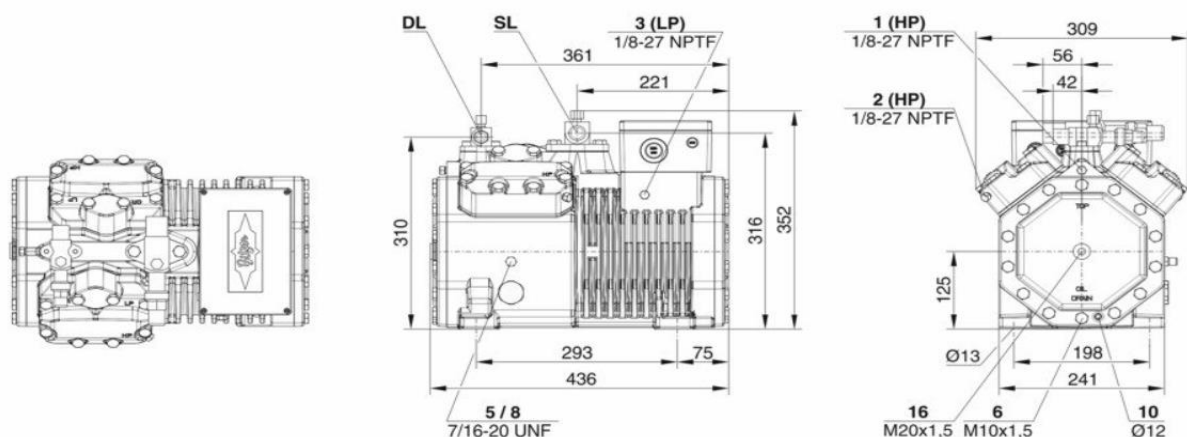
Габаритні розміри компресора 4DES-5Y
